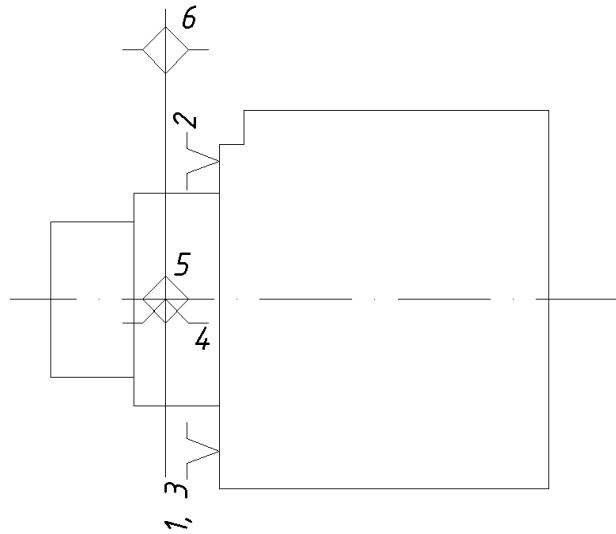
Схема базування заготовки при обробці отвору $\text{Ø}80^{+0,06}$
